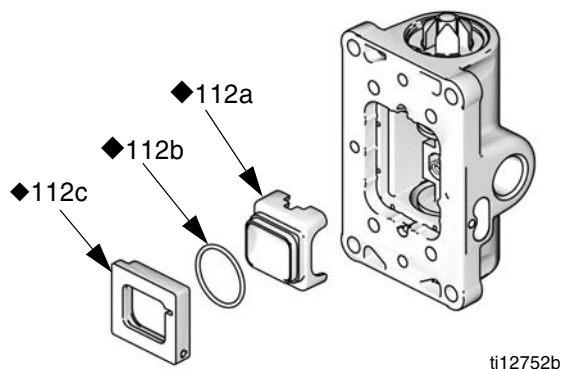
Установка уплотнений П-образного сечения в воздушный клапан
